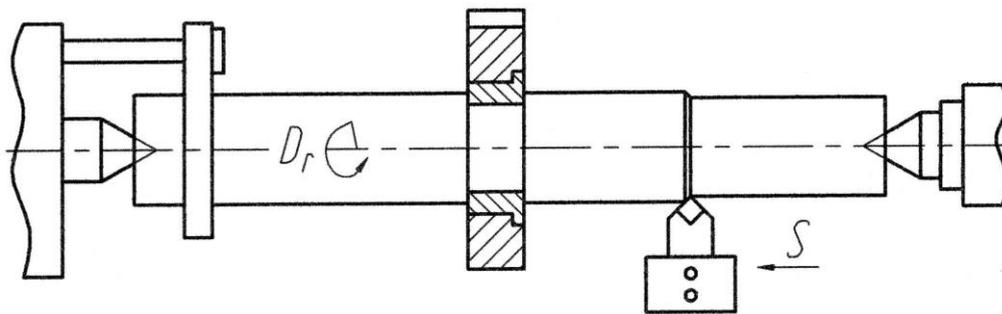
Установка заготовки с дополнительной опорой на неподвижный люнет
